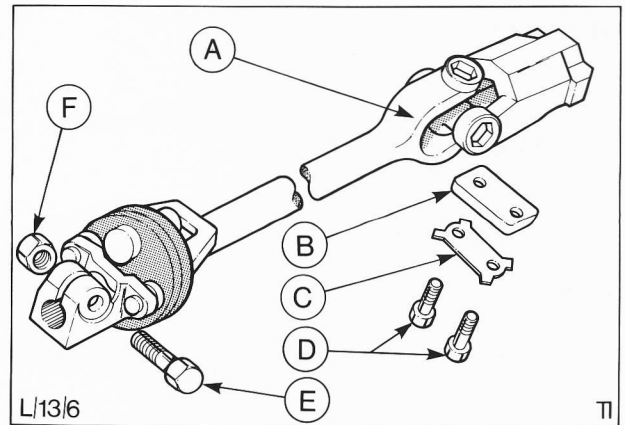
A = Kreuzgelenk D = Klemmschrauben
